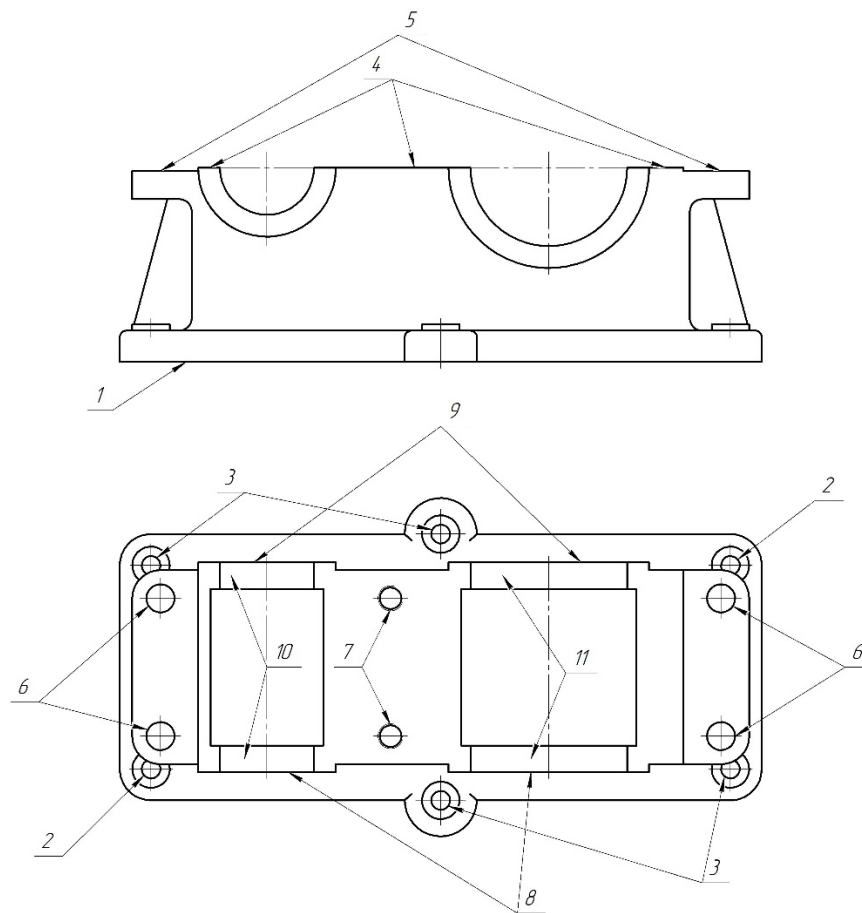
Ескіз деталі «Корпус редуктора» з пронумерованими оброблюваними поверхнями.
